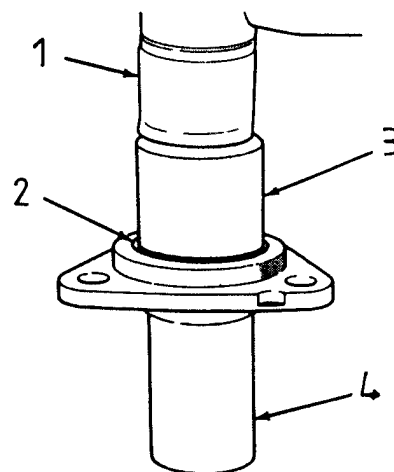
Installieren einer neuen Getriebeeingangswellen-Dichtung
